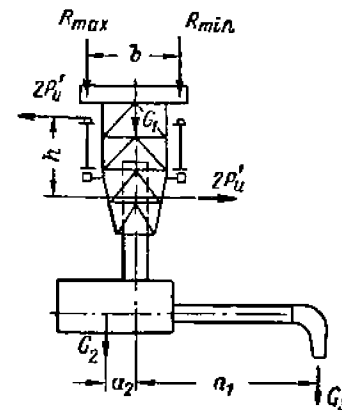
Вертикальные нагрузки на главные балки у крана с жестким подъемом груза при учете инерционных сил
